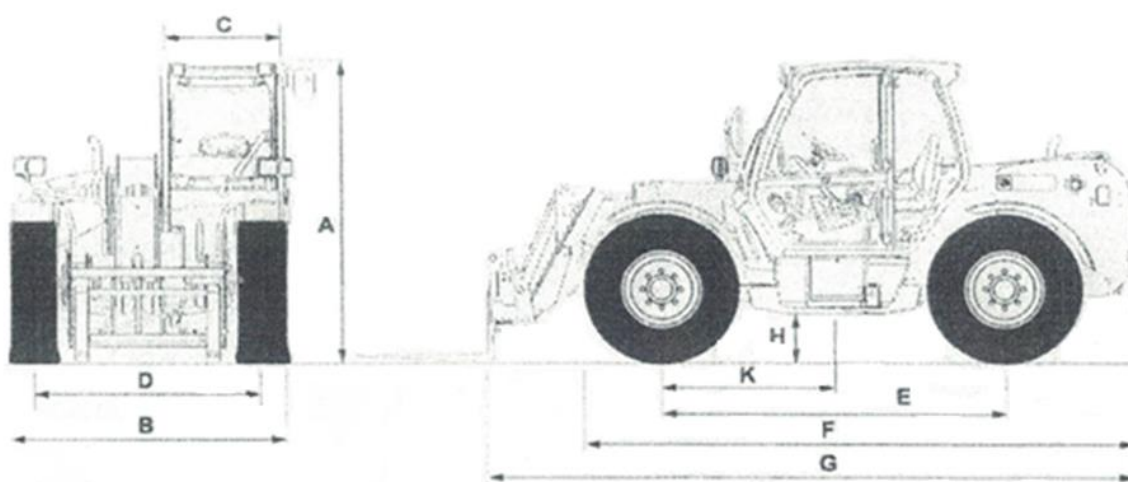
Technické parametry JCB 535-95 AGRI [11]
